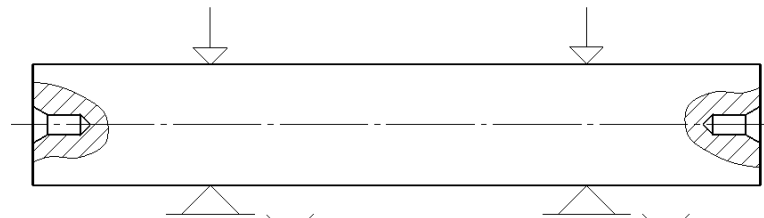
1. Схема базування при фрезерно-центрувальній обробці
